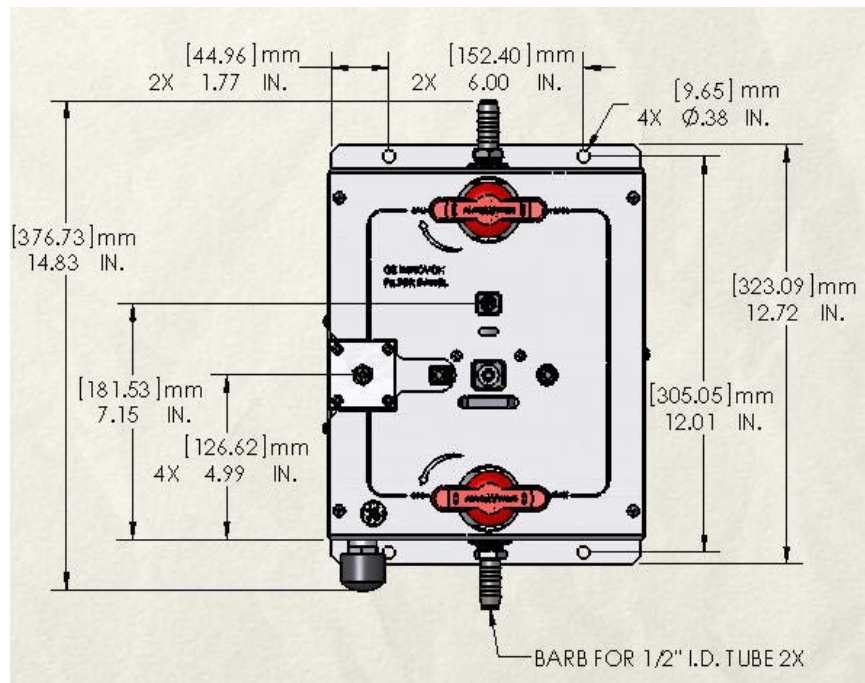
Panneau de filtre (vue de face) – Espaces nécessaires
